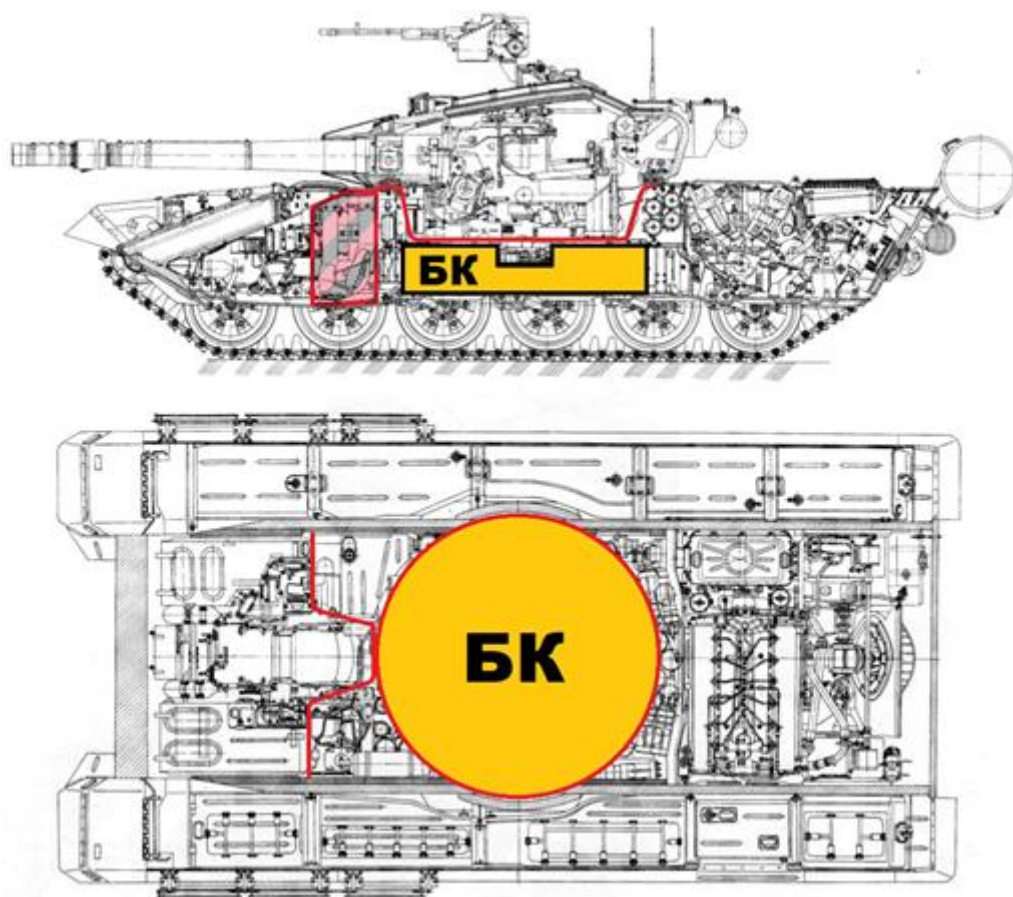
Схема расположения защитных перегородок в корпусе танка Т-72
